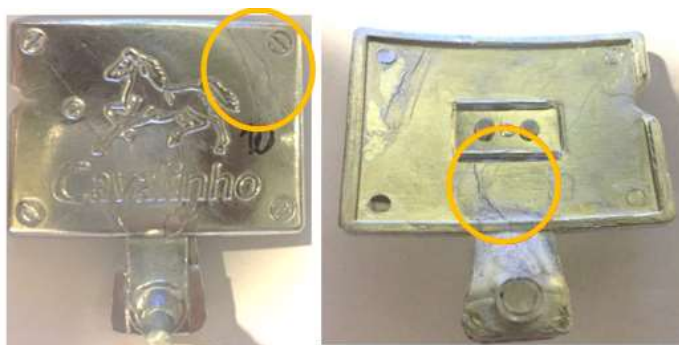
Ensaio C10 - MZ3P05TE6TA005TS05MS – Peça com fissuras e preenchimento deficiente
